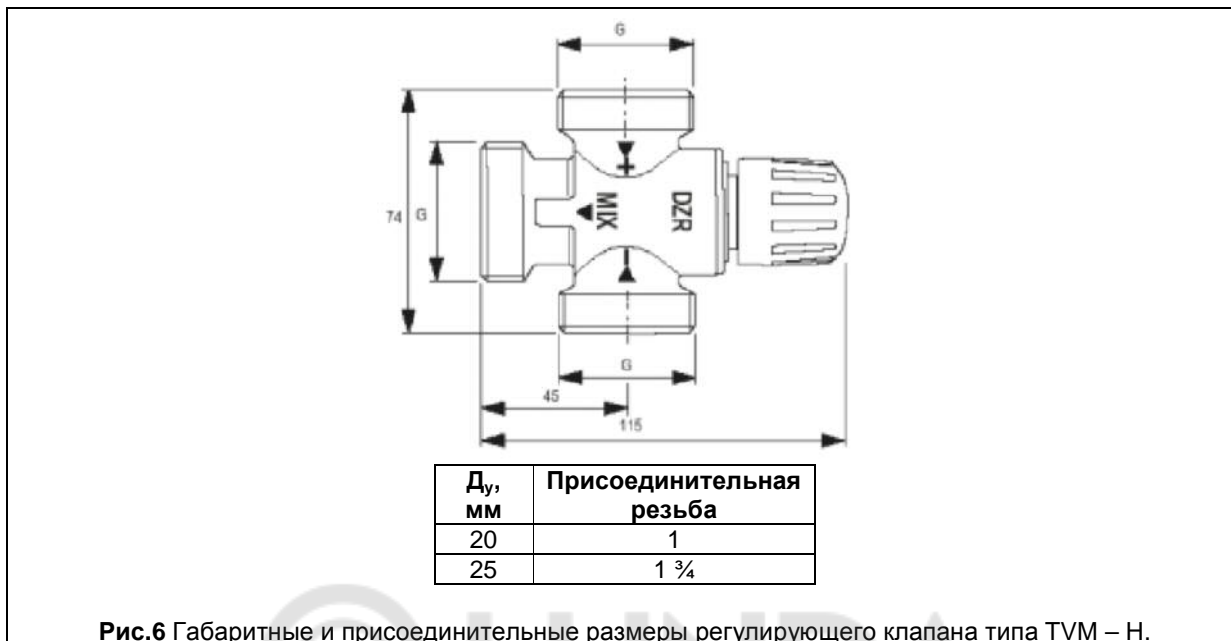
Габаритные и присоединительные размеры регулирующего клапана типа TVM – Н.
